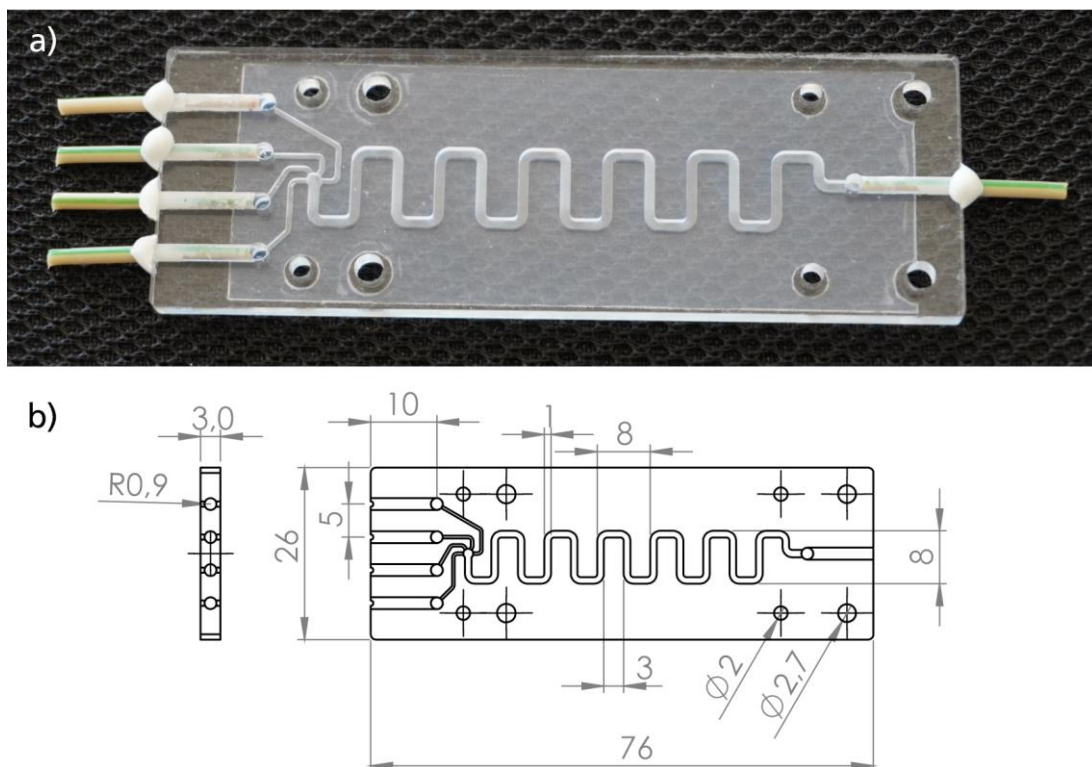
(a) Gedeckelter und mit Anschlusskapillaren versehener Fluidchip der Systemvariante B. (b) Fertigungszeichnung des Fluidchips mit den wichtigsten Maßen.
